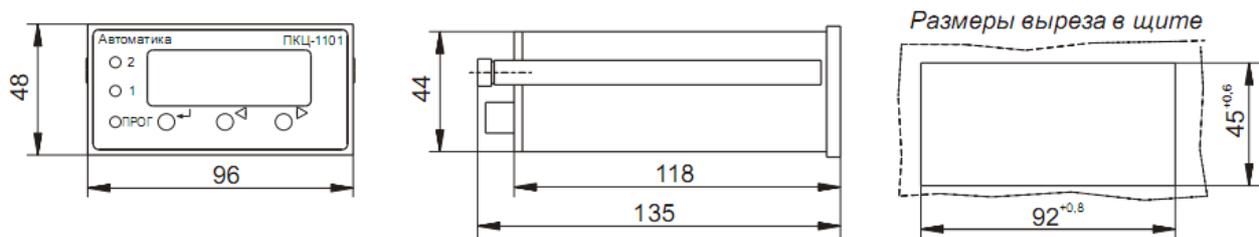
Габаритные размеры прибора ПКЦ-1101
